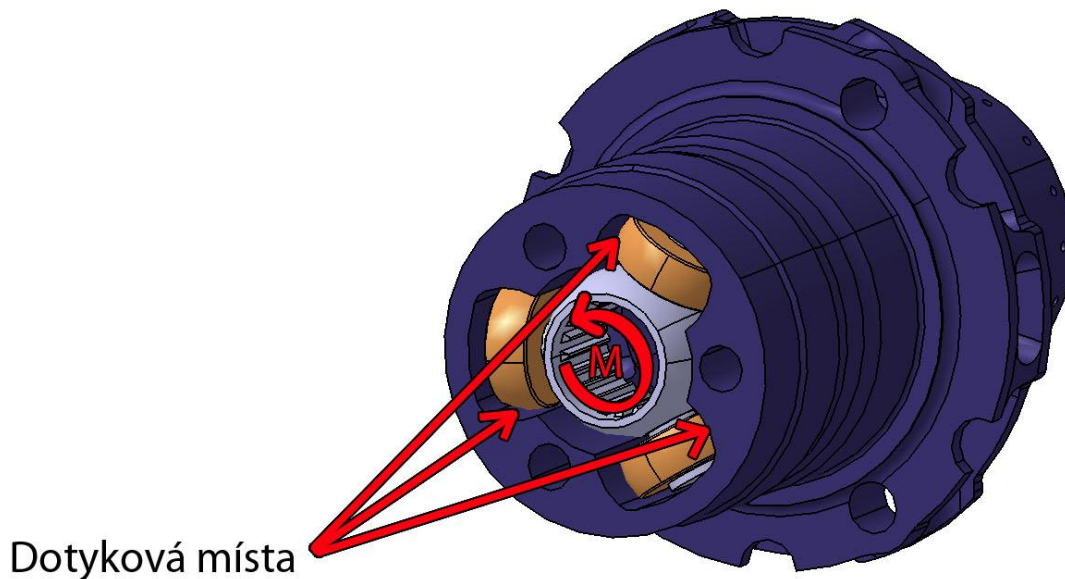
Detail řezu sestavy s ložiskovou maticí
